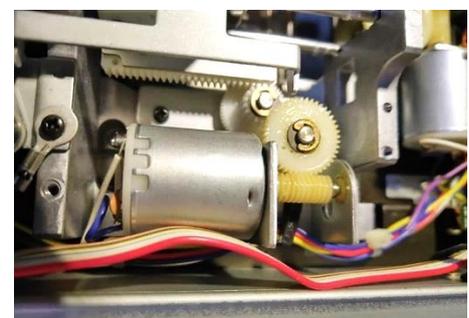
Sled-Motor mit Zahnstangengetriebe<sup>51</sup>
